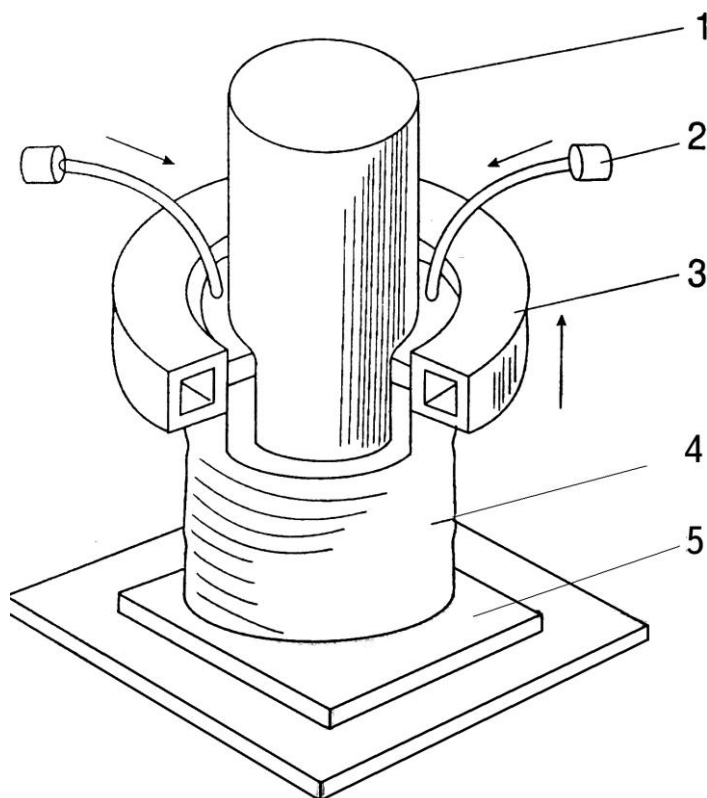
ЭШН цилиндрической наружной поверхности при большой длине образующей:
